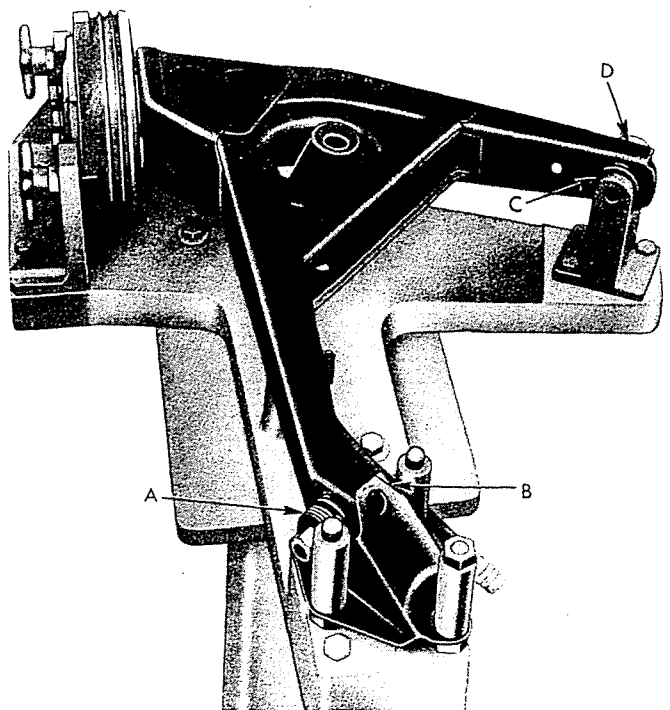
Einstellung des linken Längslenkers auf dem Werkzeug A. 66064.
